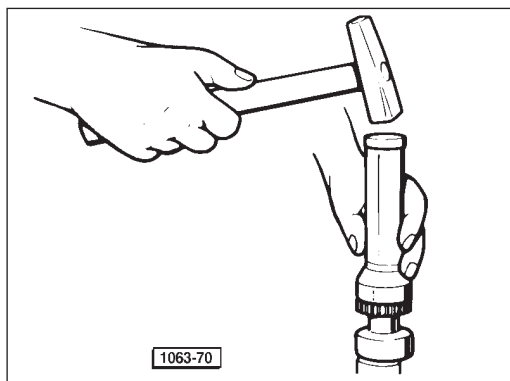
Montage de l'engrenage de commande du régulateur.
